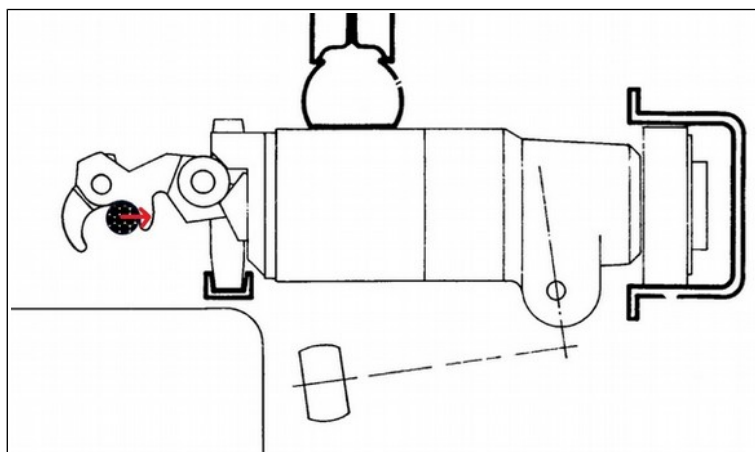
schéma du câble décalé latéralement en contact avec le bec du mors mobile
